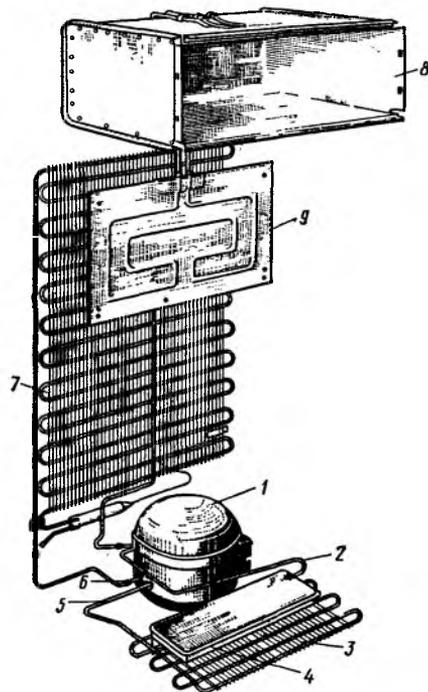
Двухиспарительный компрессионный холодильный агрегат с охладителем масла:
